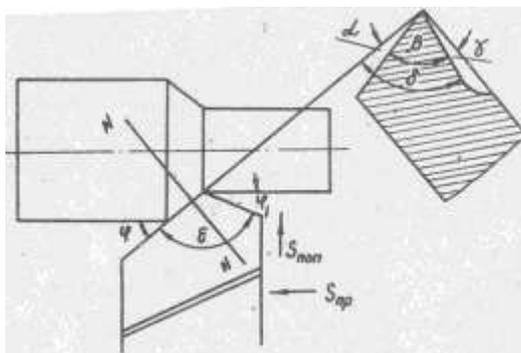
Геометрические параметры токарного проходного резца
